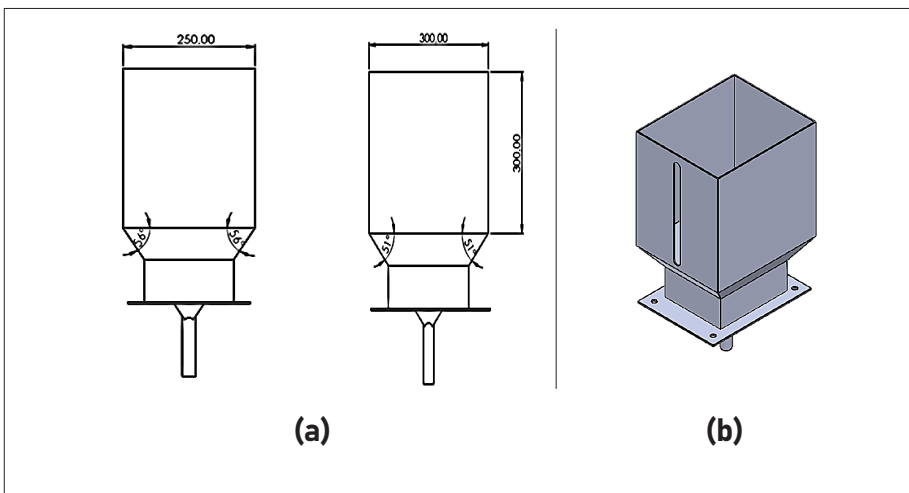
(a) Dimensiones de la tolva; (b) Diseño final de la tolva de arena.
